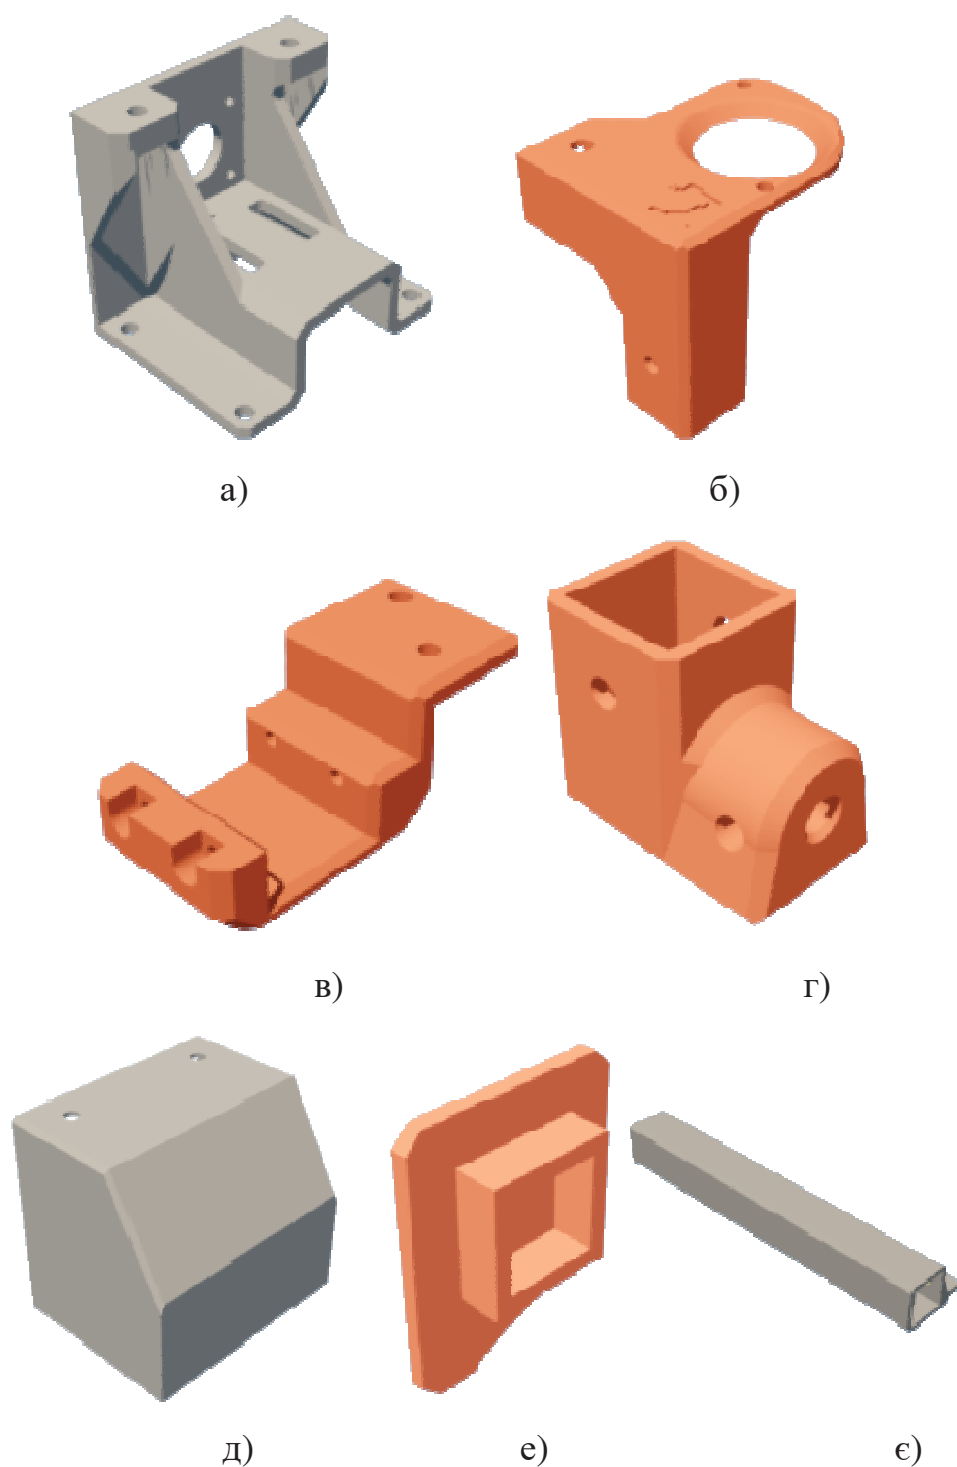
Основні деталі спроектовані у середовищі SolidWorks: а - тримач поворотного крокового двигуна механізму ножа; б - кріплення обдуву; в - монтажний кронштейн кріплення механізму вилучення виробів; г - муфта поворотного механізму; д – захисний кожух; е – тримач напрямляючої; ж – ніж зі кріпленням
